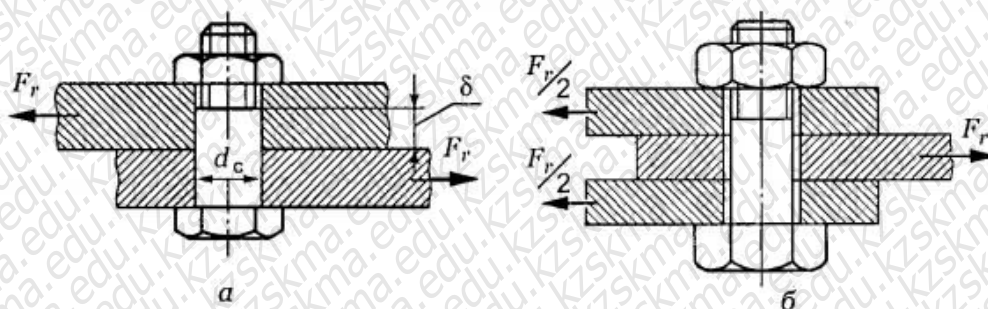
Схема к расчету затянутого болта под действием поперечной силы:
